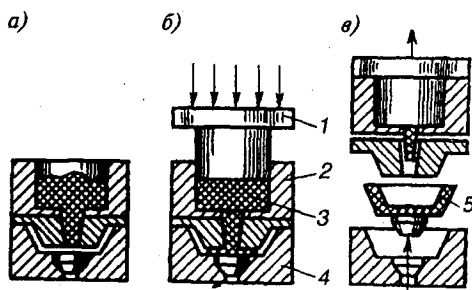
Схема литьевого прессования: а — пресс-форма нагрета и закрыта; б — подача расплавленного материала в пресс-форму; в — разъем пресс-формы; 1 — пуансон; 2 — загрузочная камера; 3 — пресс-материал; 4 — пресс-форма; 5 — готовое изделие
